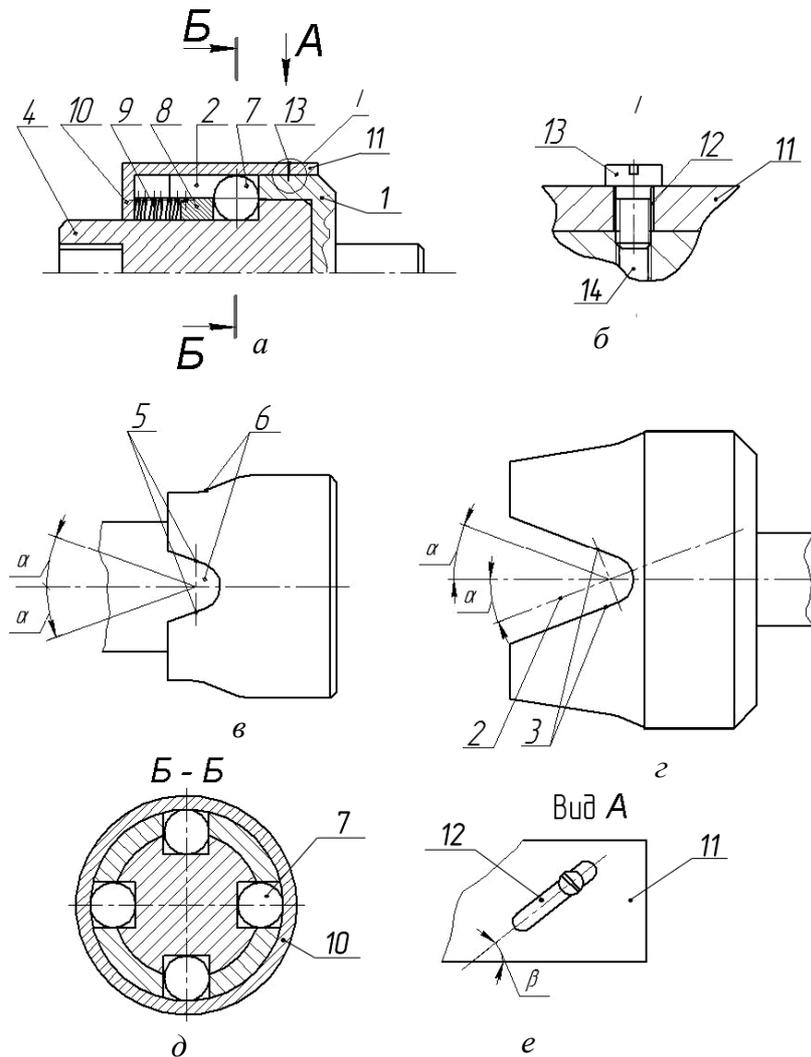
Конструкція нового обмежувача оберального моменту: а – загальний його вигляд в розрізі; б – в місці І; в – ведена напівмуфта; г – ведуча напівмуфта; д – переріз Б-Б; е – вид А
